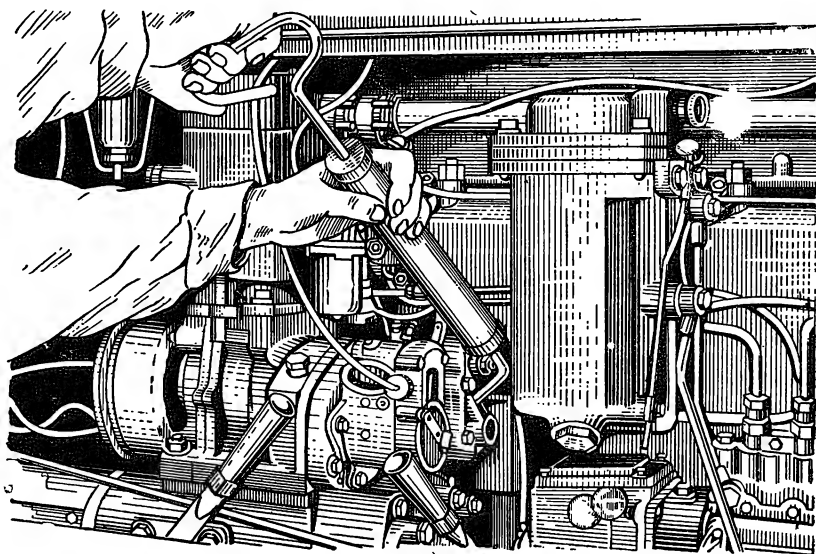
Заправка маслом корпуса регулятора пускового двигателя
